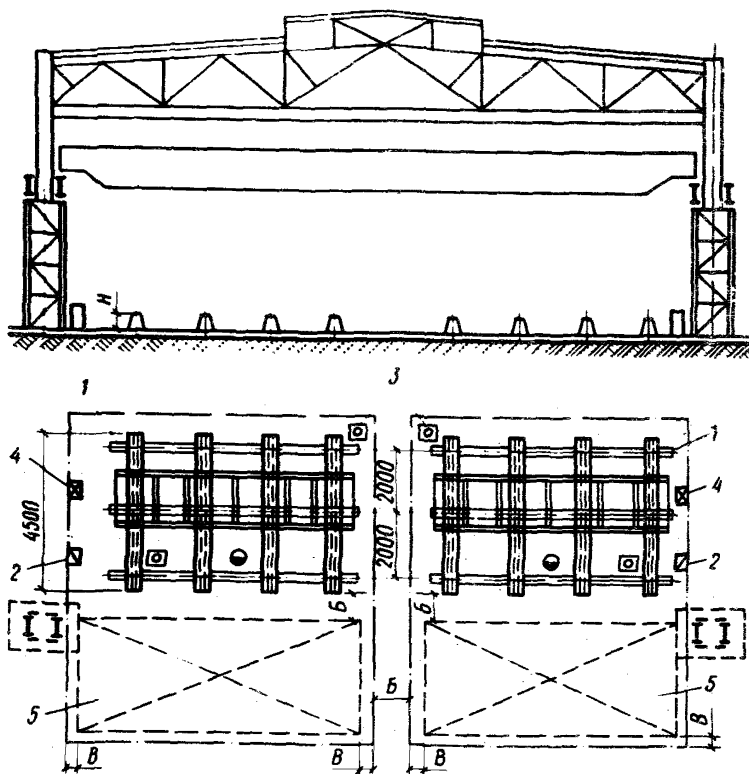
Размещение стенда для сварки из козлов в поперечном пролете
